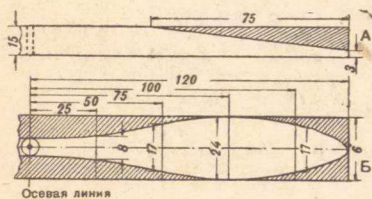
Чертеж винта: А — боковой шаблон, Б — верхний шаблон.
